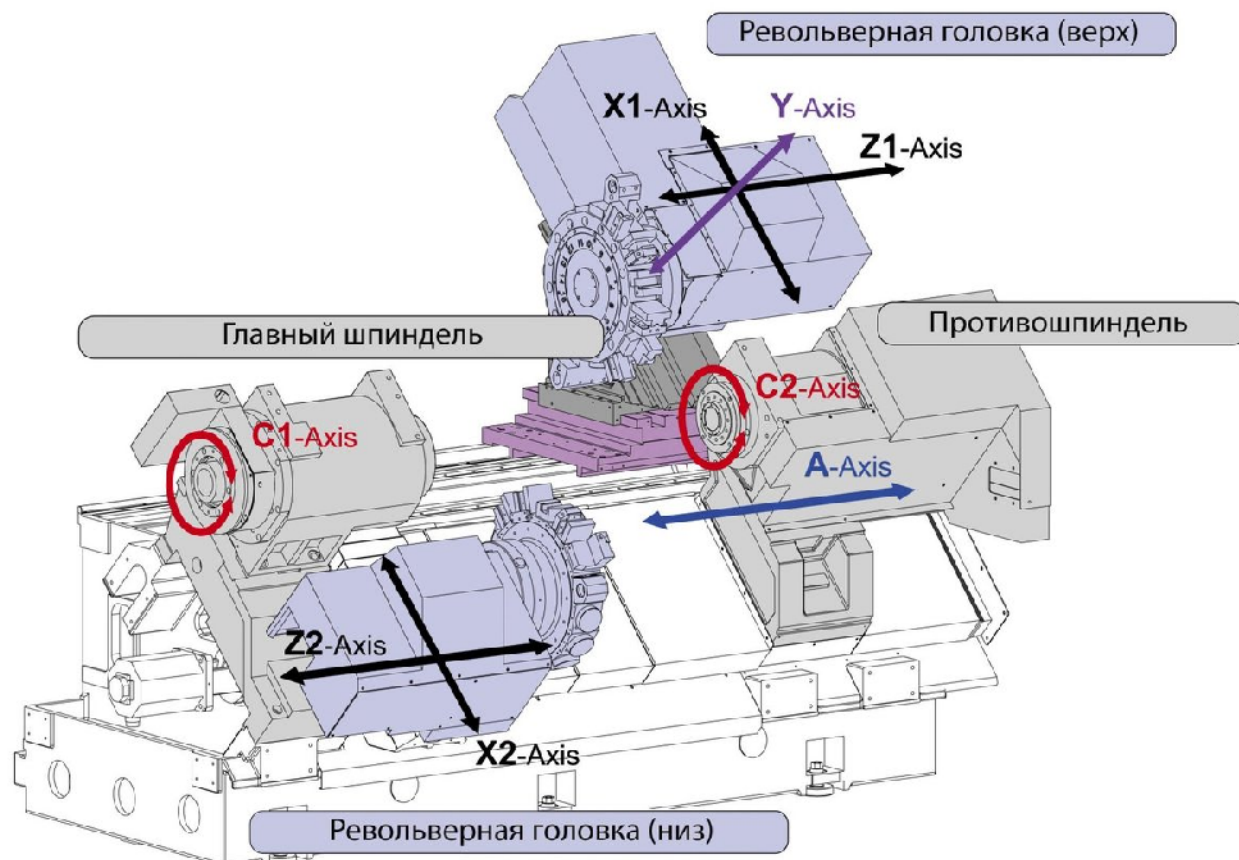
Токарно-револьверный станок с двумя револьверными головками
